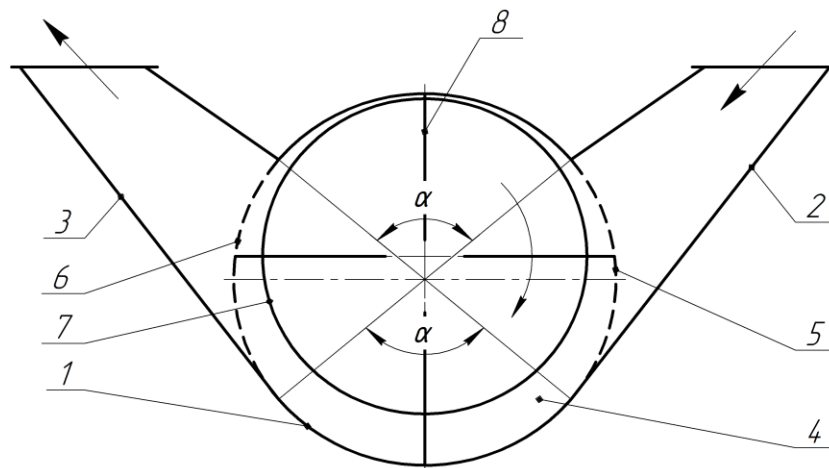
Схема розміщення впускного та випускного вікон в робочій камері вакуумного насоса: 1 – корпус; 2 – впускний патрубок; 3 – випускний патрубок; 4 – робоча камера; 5 – впускне вікно; 6 – випускне вікно; 7 – ротор; 8 – лопатки.
